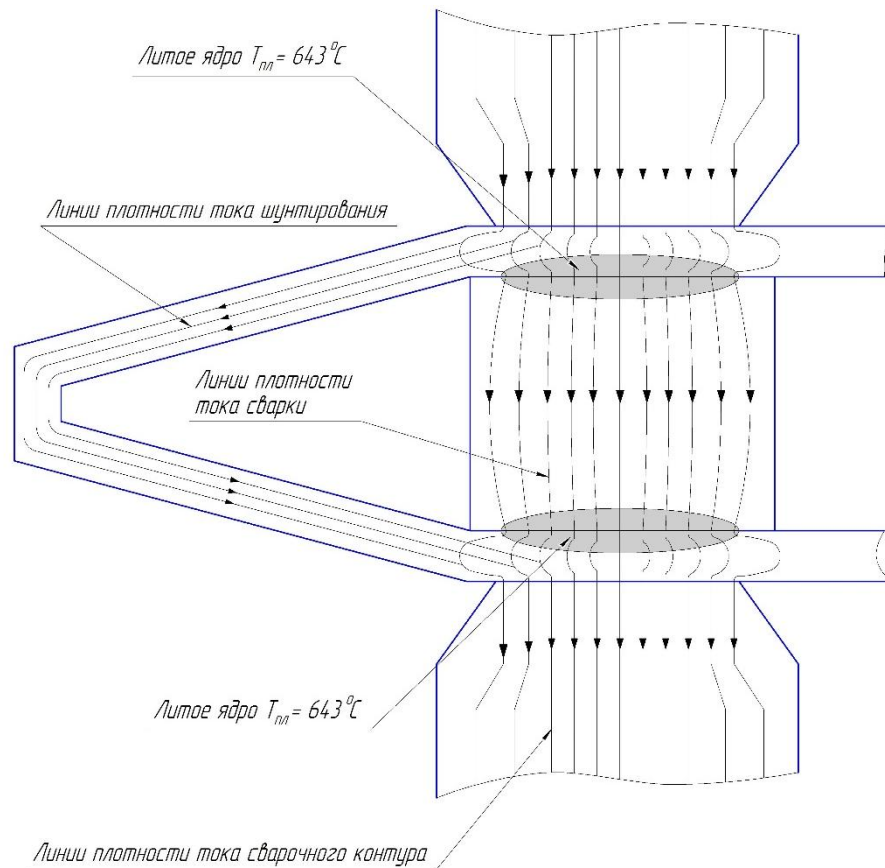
Схема протекания тока при точечной сварке антенного излучателя
